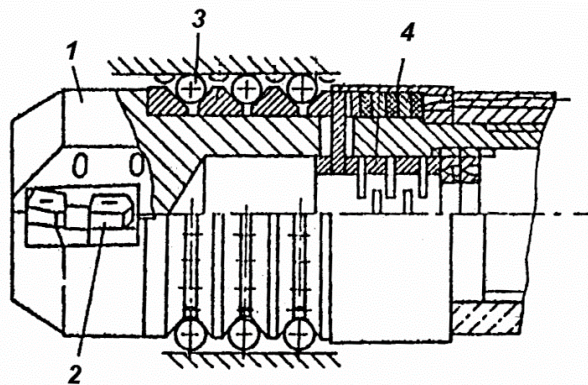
Інструмент для віброобробки глибоких отворів
